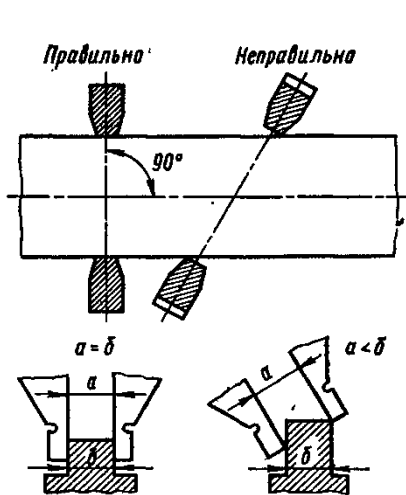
Установка штангенциркуля при измерении наружных поверхностей
